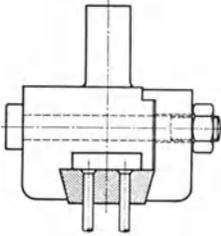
Befestigung eines Stempelfußes durch Schräge und Zugschraube.
